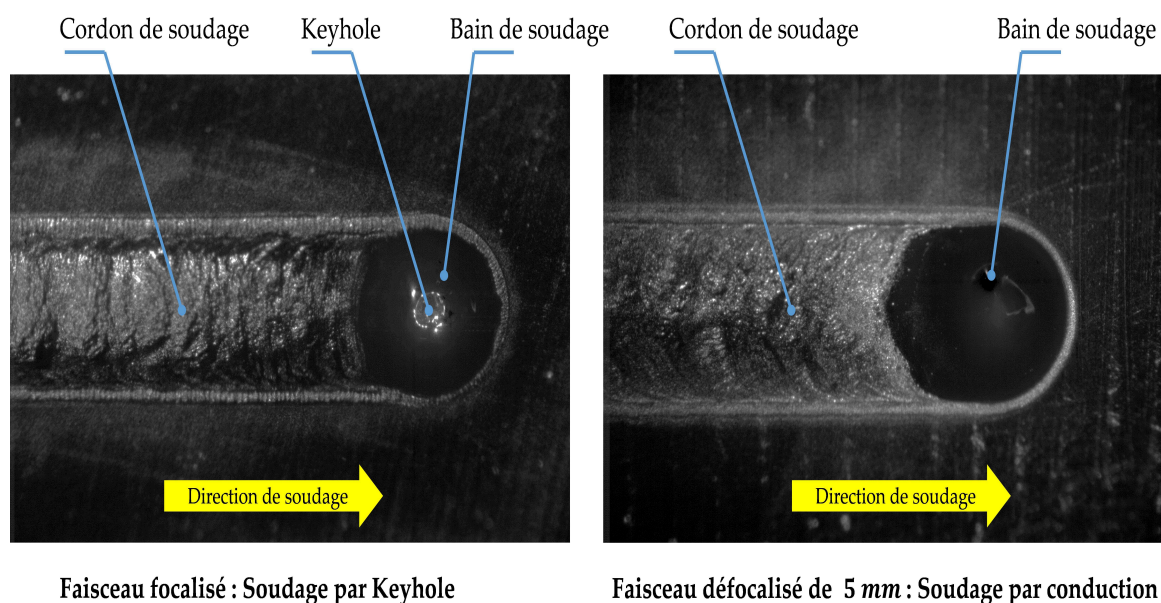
Deux configurations de soudage : soudage par Keyhole et soudage par conduction.
